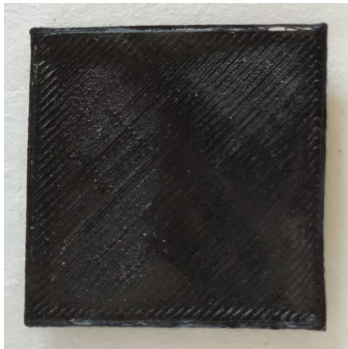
Placa impresa boq.0,4mm, ec=0,1mm
